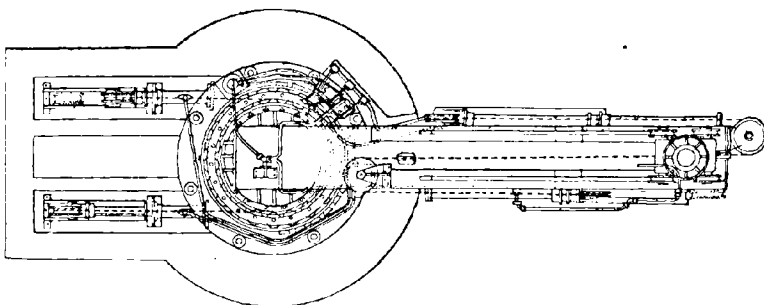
Grue hydraulique de 40 tonnes (plan horizontal).
